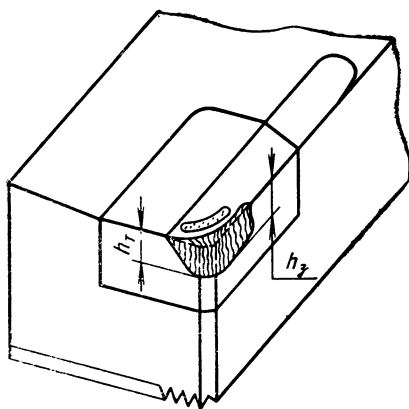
Схема износа зубьев твердосплавных фрез, h_z — износ по задней поверхности; h_T — износ по торцу ножа.
